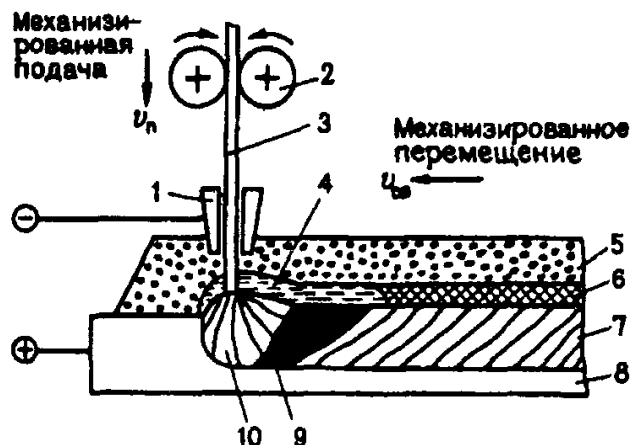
Схема процесса автоматической дуговой сварки под флюсом
